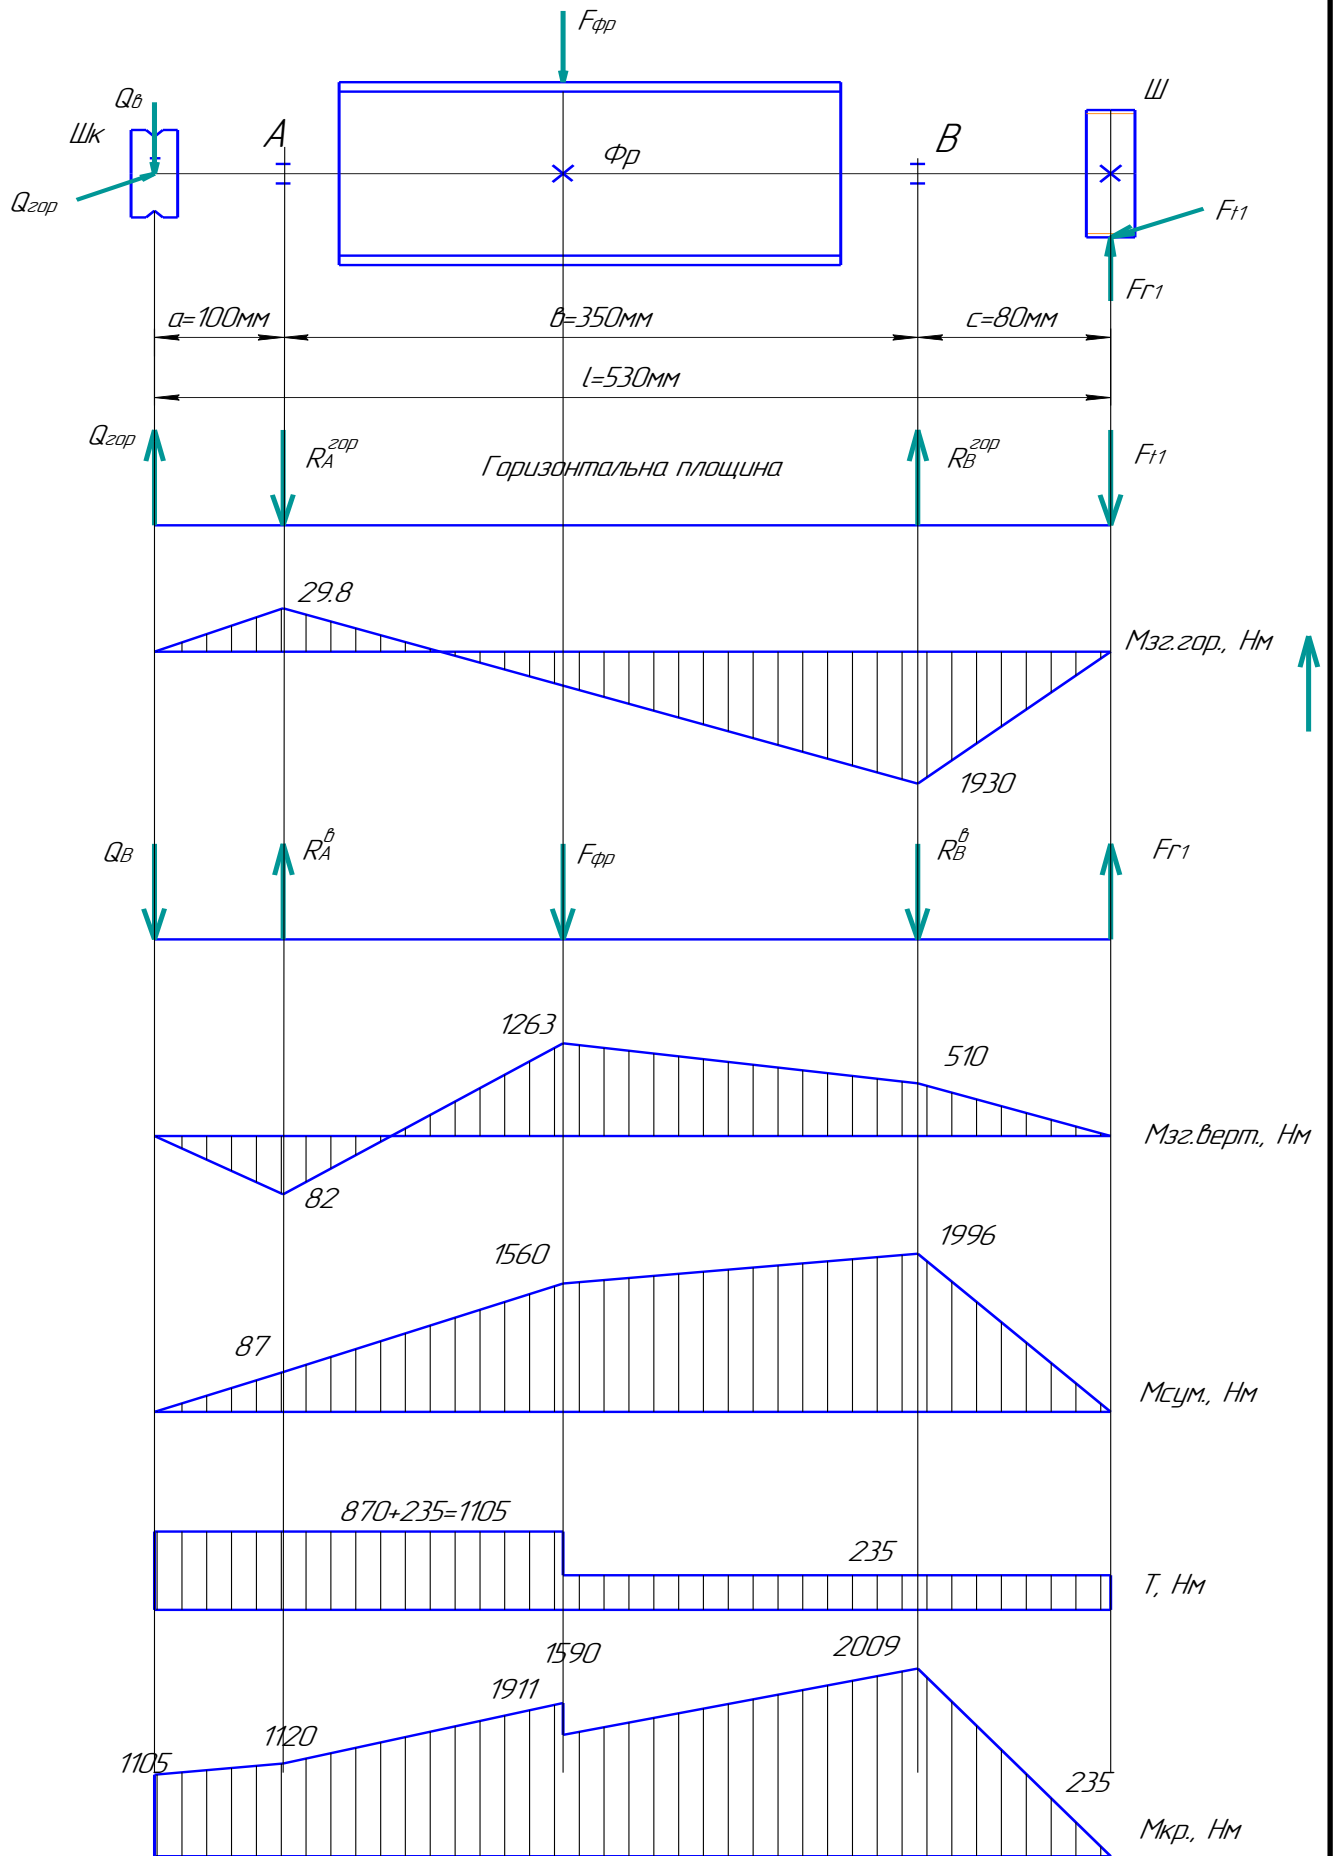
Розрахункова схема і епюри моментів вала - фрези
